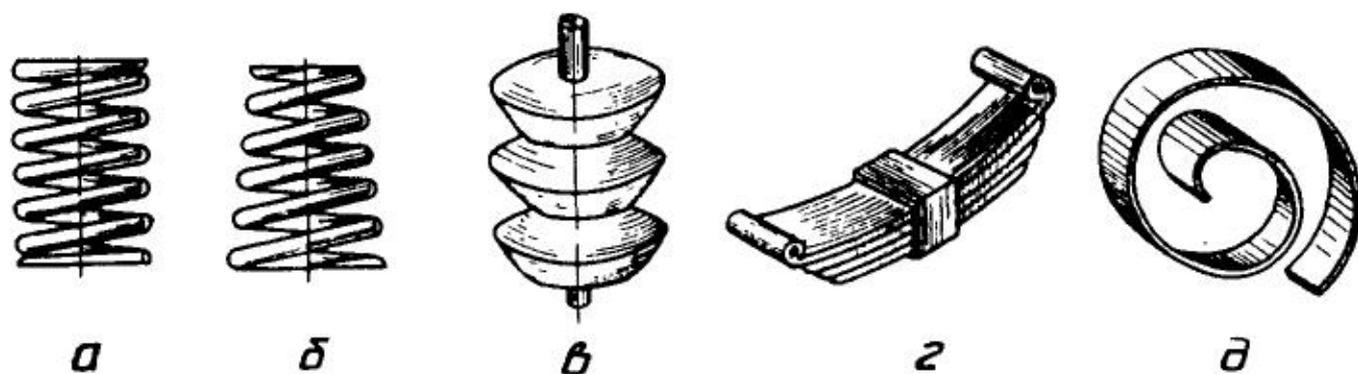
Форми пружин: *а* — циліндрична; *б* — конічна; *в* — тарілчаста; *г* — пластинчаста; *д* — спіральна.
